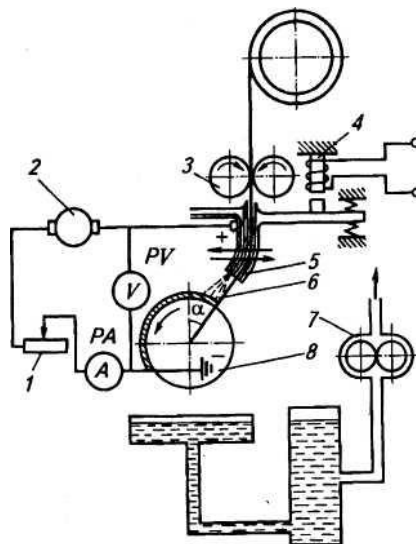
Принципиальная схема установки для вибродуговой наплавки:
